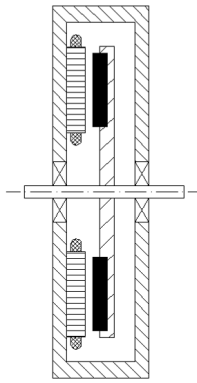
Rotor se symetrickým magnetickým tokem
